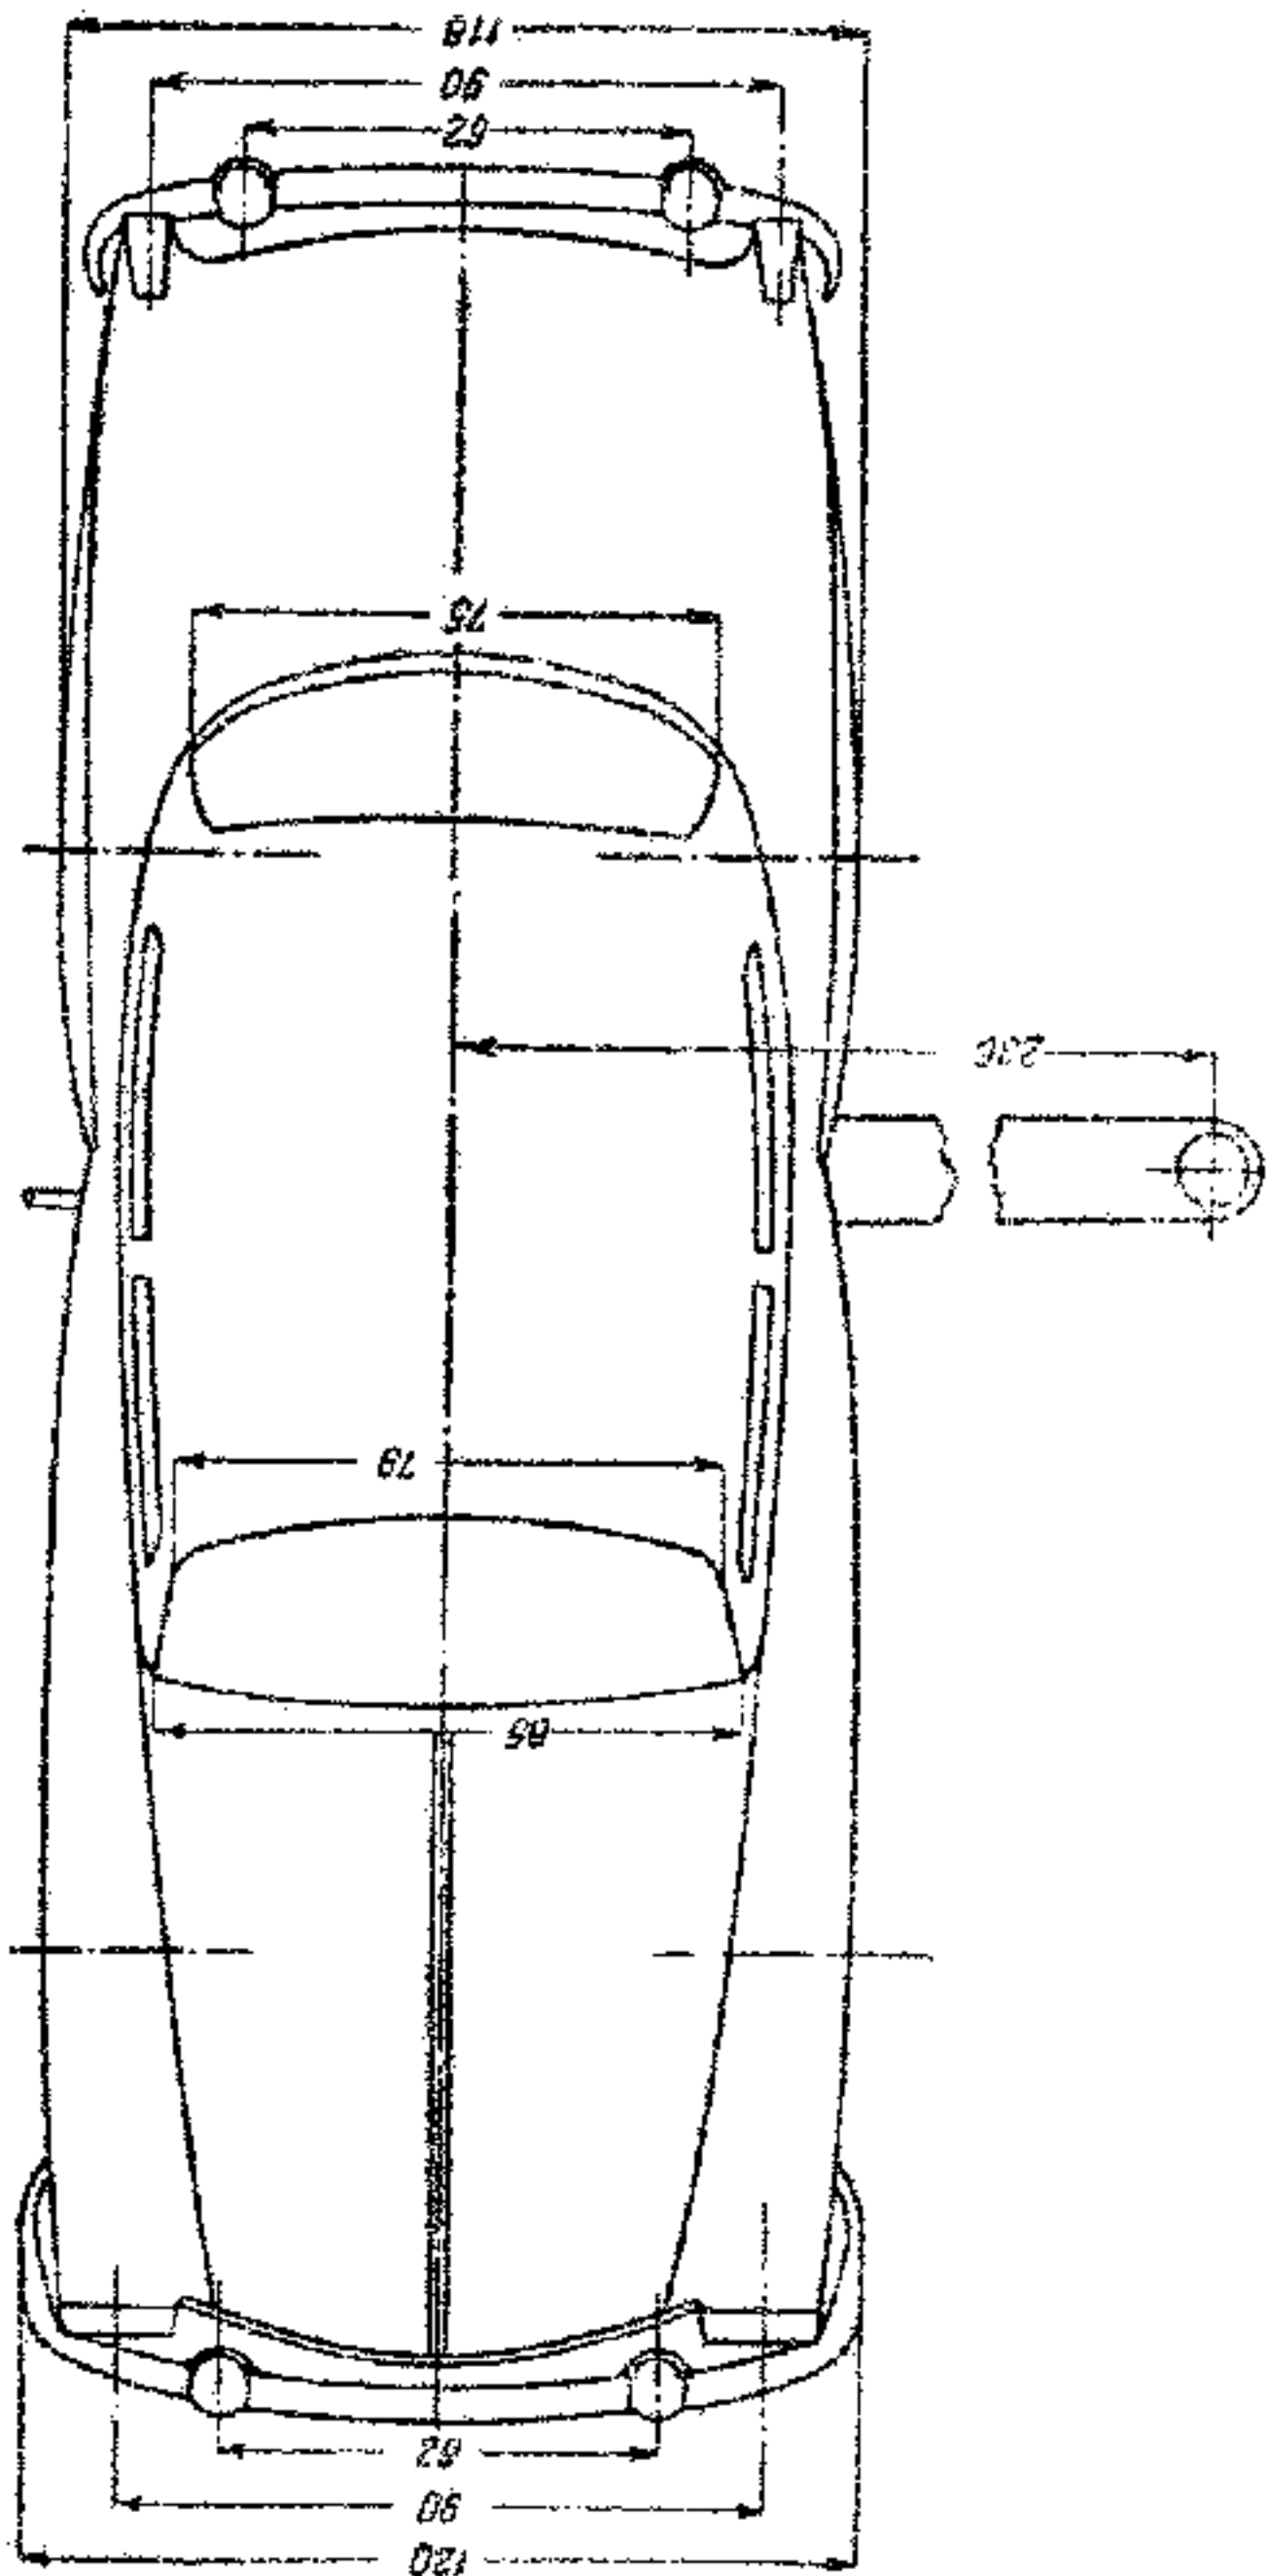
ОБЩИЙ ВИД МОДЕЛИ (ВИД СВЕРХУ)
